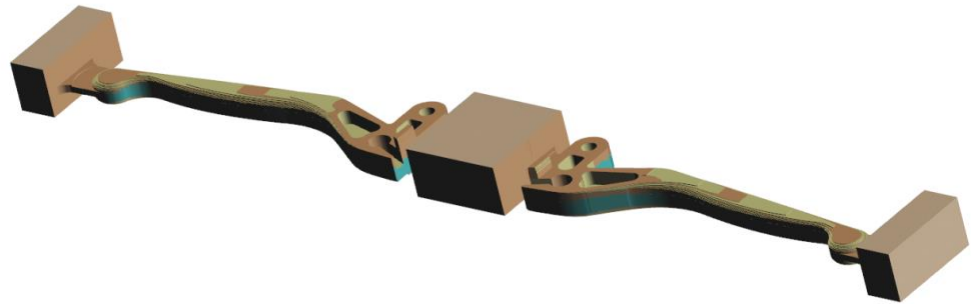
Brzdové páčky po hrubování ve druhém upnutí
